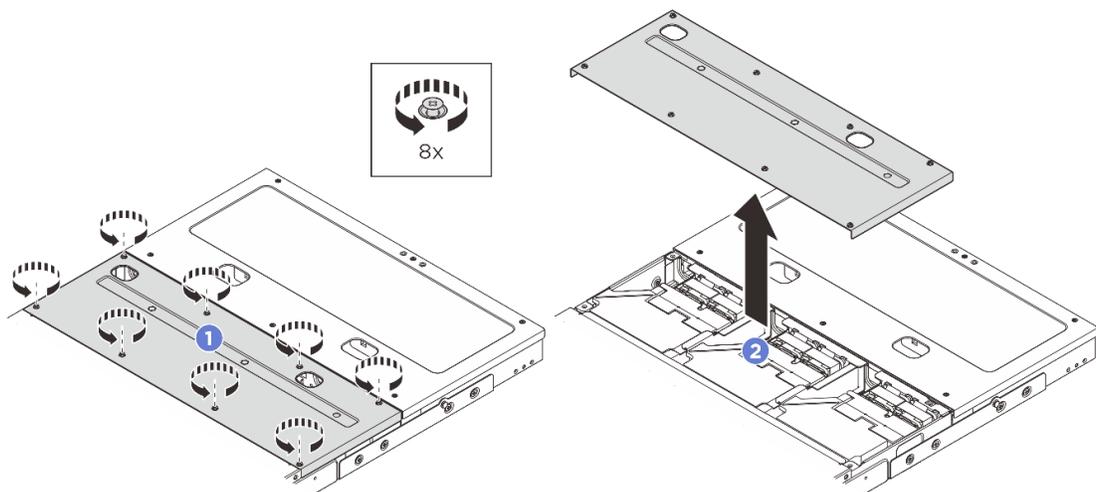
Extracción de la cubierta superior central del alojamiento 1U3N
